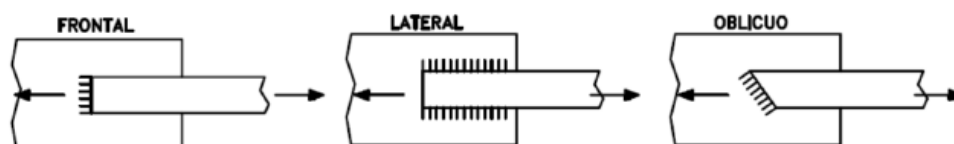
Clasificación del cordón de soldadura por la posición de este respecto al esfuerzo.
